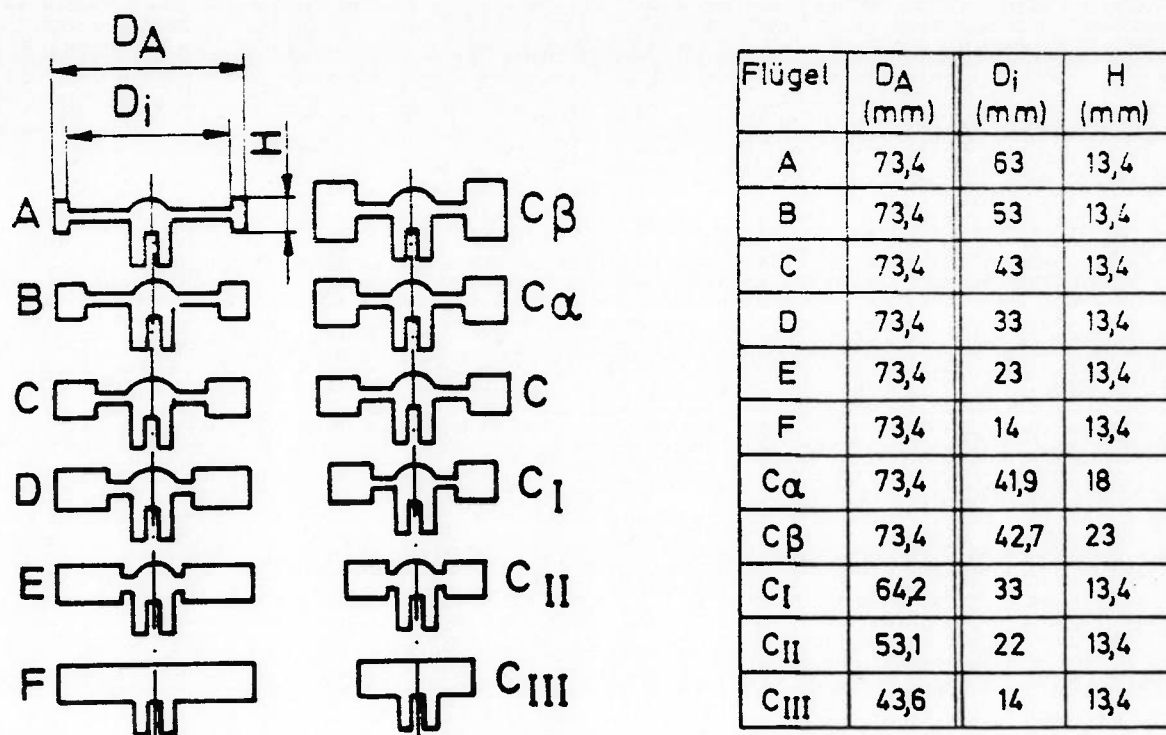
Formas e dimensões das pás utilizadas nos levantamentos de Frank [15]. Diâmetro do cilindro $D = 80$ mm.
